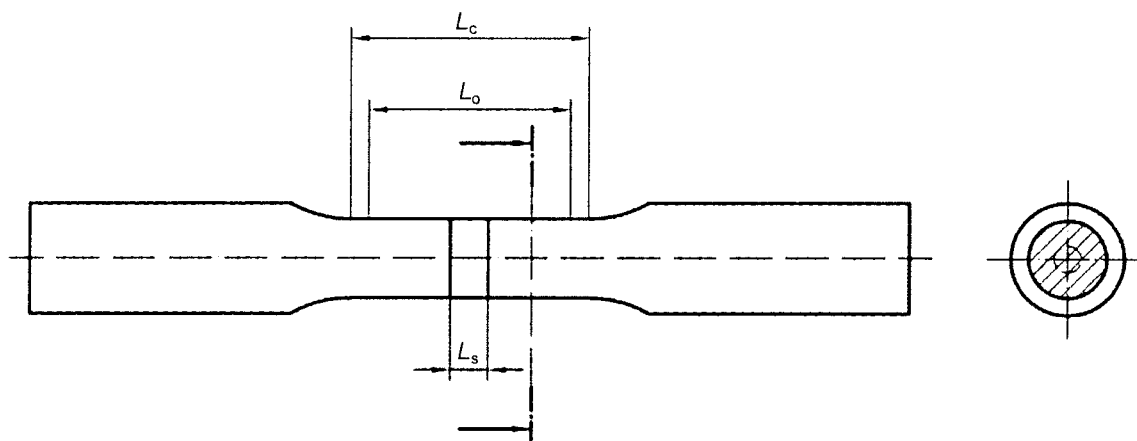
Циліндричний випробний зразок із заготовки суцільного прямокутного перерізу
